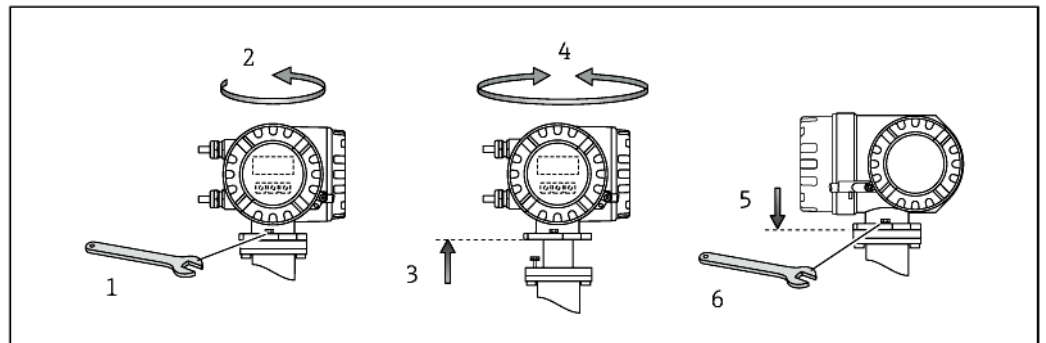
Вращение корпуса трансмиттера (алюминиевый полевой корпус)
